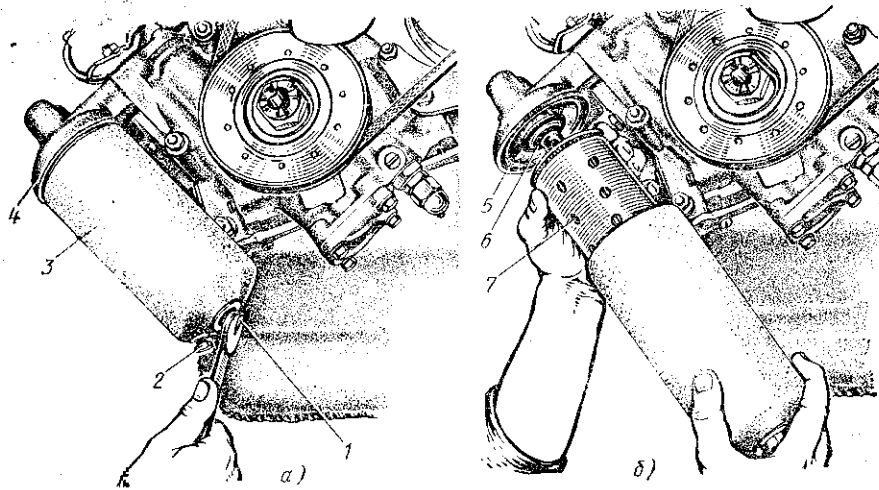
Операция замены фильтрующего элемента системы смазки двигателя: а — снятие корпуса фильтра; б — удаление фильтрующего элемента; 1 — болт крепления; 2 — пробка; 3 — корпус фильтра; 4 — крышка корпуса; 5 и 6 — уплотнительные кольца; 7 — бумажный фильтрующий элемент
